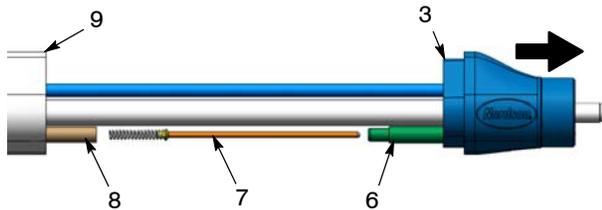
Smontaggio del resistore – Pistole con montaggio su tubo
